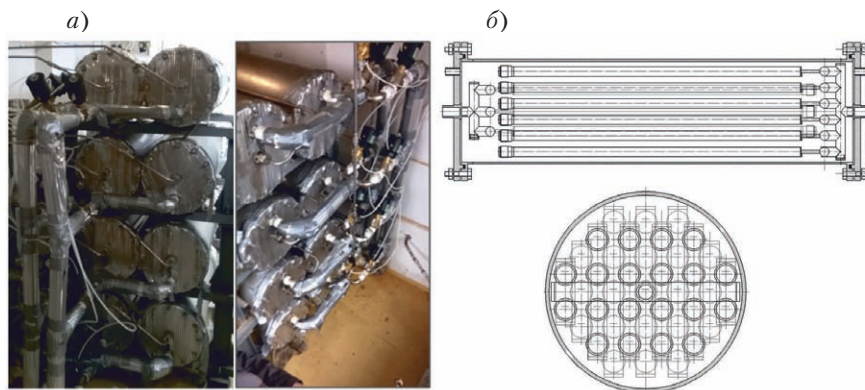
Общий вид компрессора ТСК2-3,5/150 (а) и схема его металлгидридного модуля (б)
